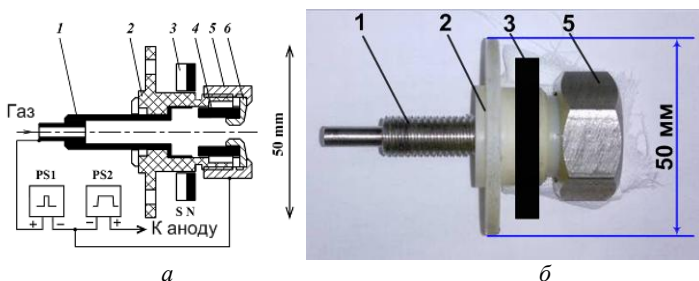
Конструкция катодного узла (а) и его внешний вид (б): 1 – поджигающий электрод; 2 – изолятор; 3 – кольцевой магнит; 4 – магниевый полый катод; 5 – гайка из нержавеющей стали; 6 – ферромагнитная вставка
